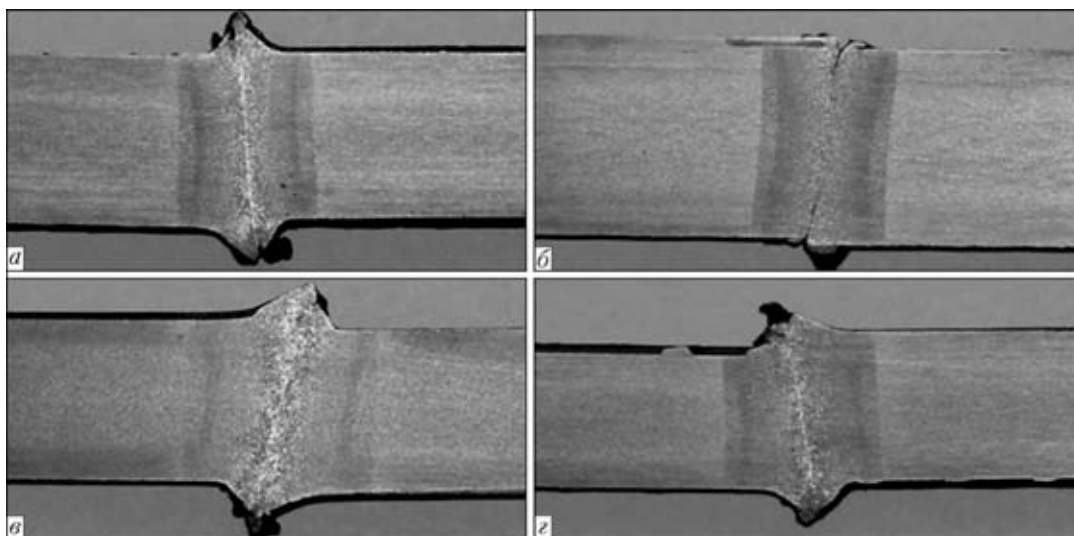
Макрошлифы стыков, полученных на различных режимах сварки: здесь и далее на рис. 2 и 3 *a* — оптимальный; *б, в* — соответственно пониженные скорость и напряжение; *г* — увеличенный вылет
